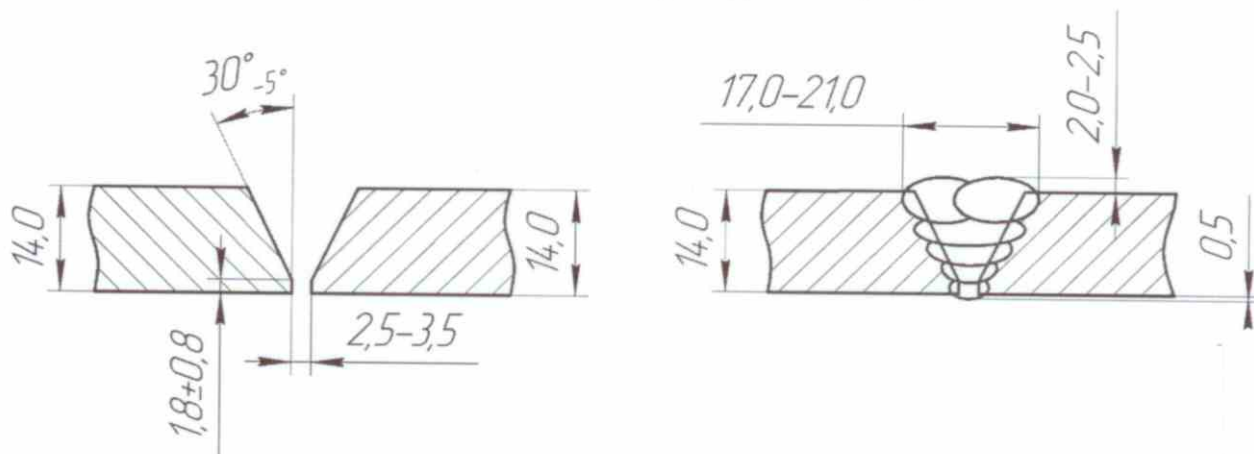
Геометрические параметры сборки и сварного шва
